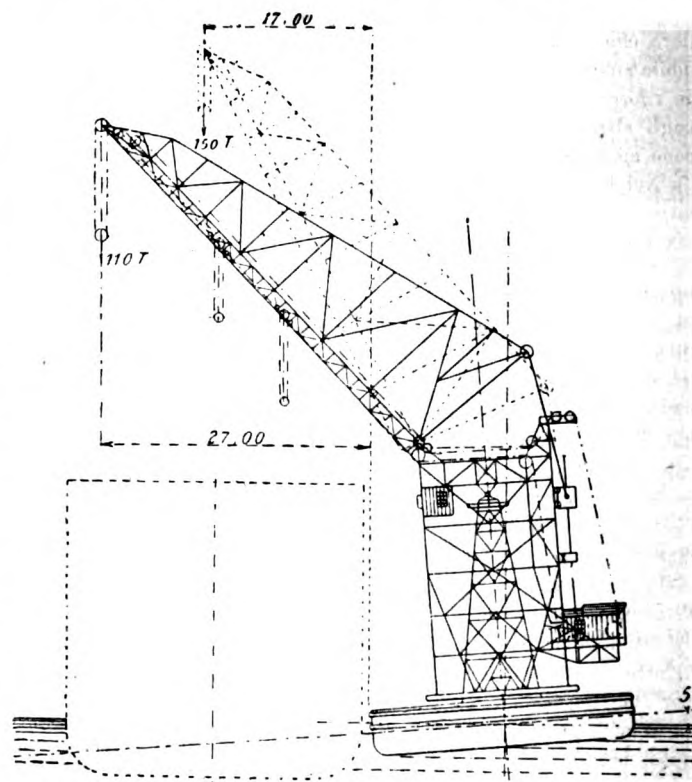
Gru galleggiante da 150 tonn. dei Cantieri Harland - Elevazione.
